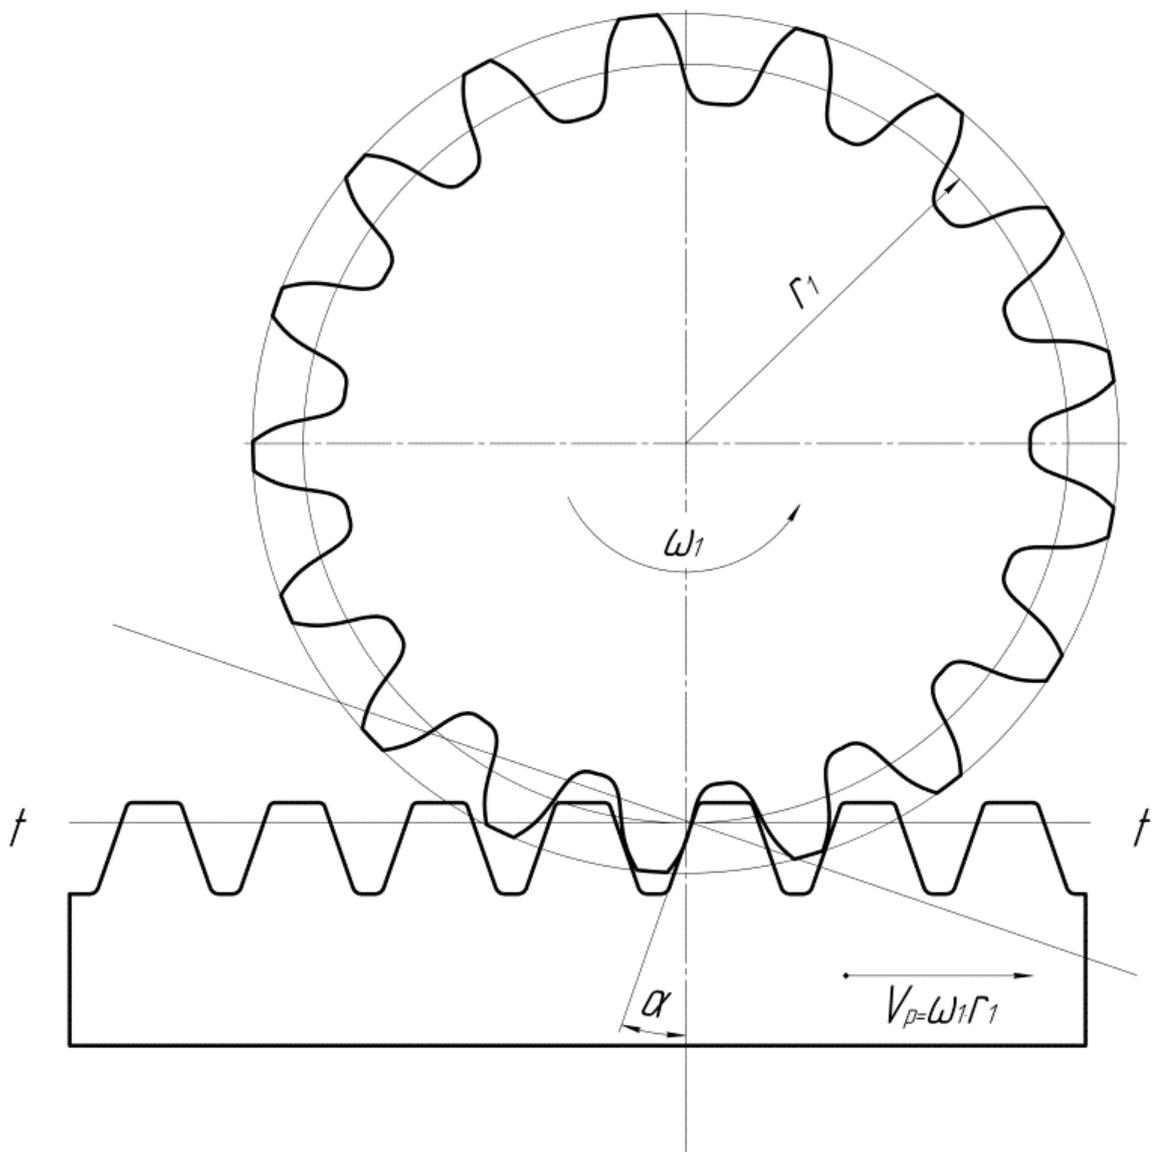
Сопряжение получаемого зубчатого колеса и инструментальной рейки
